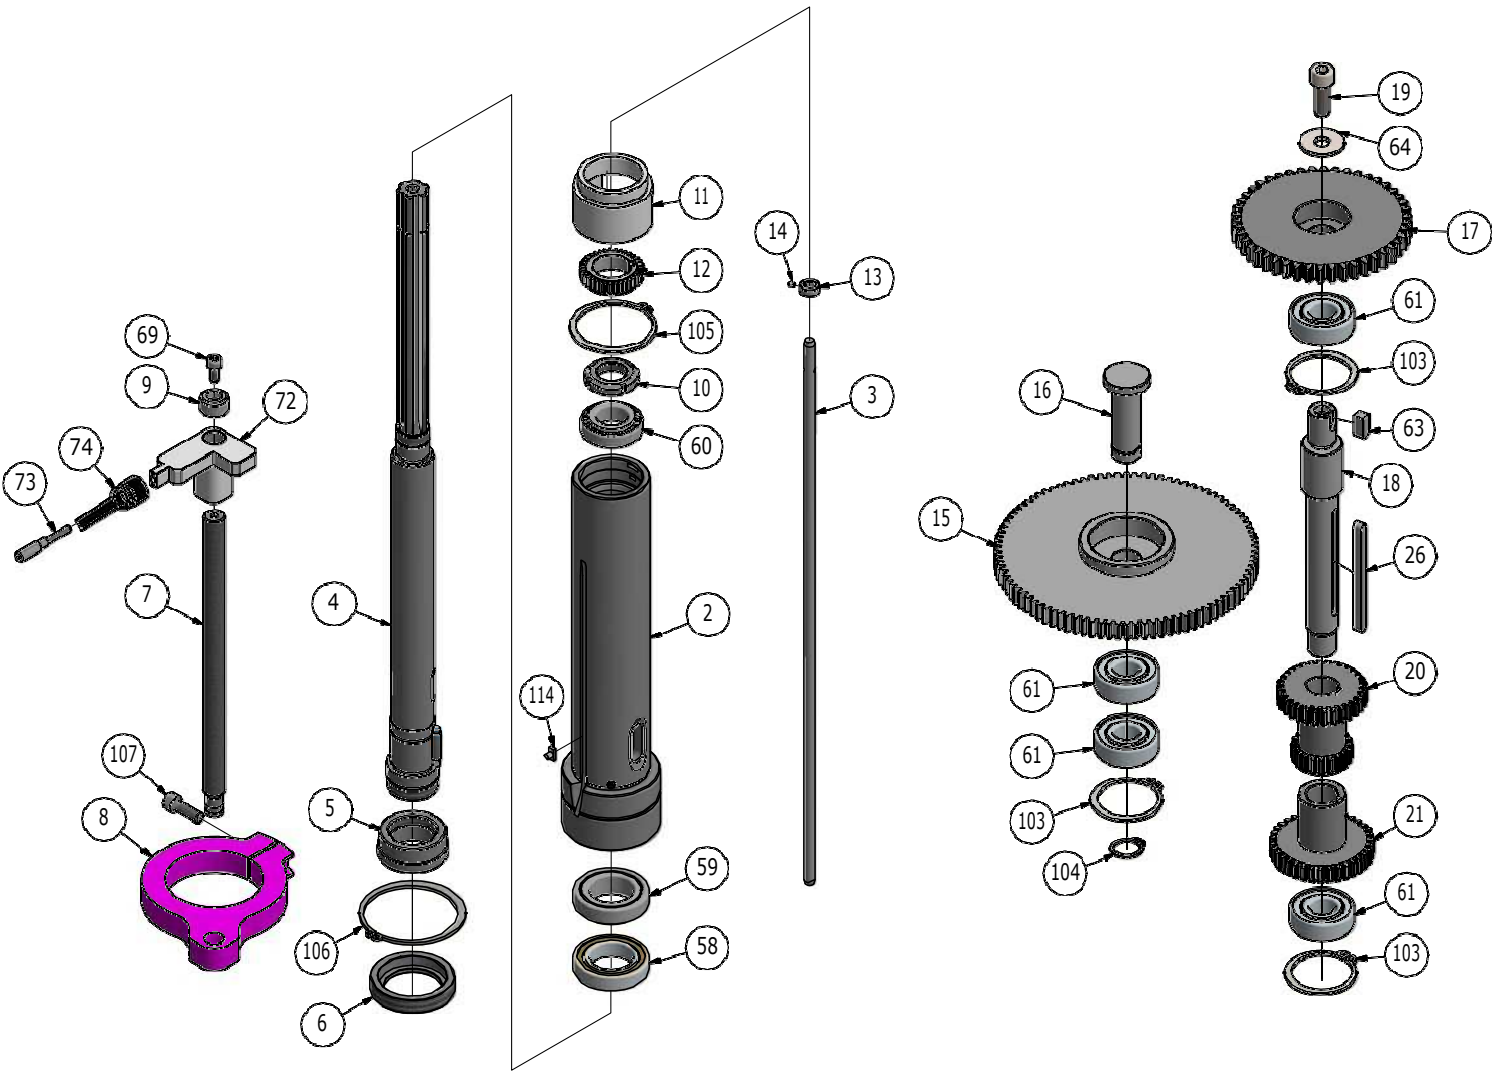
GetriebeTeilB - Elemento de engranaje B
